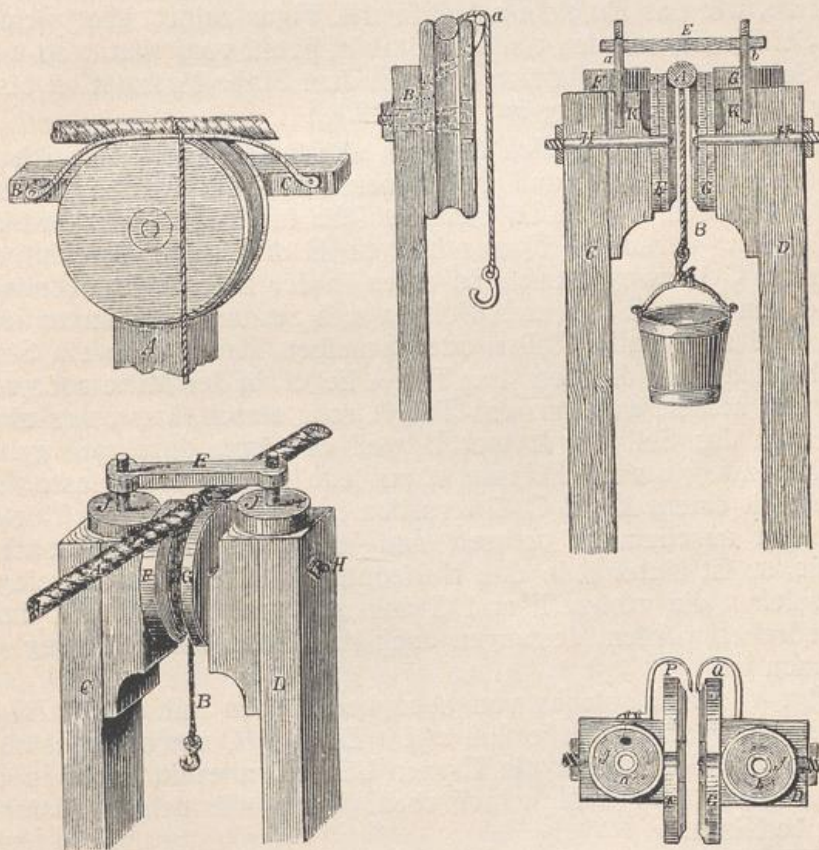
Leupold, 1724, Einzelheiten, Aufhängung der Eimer, Rollenführungen zu Dantziger Maschine.
